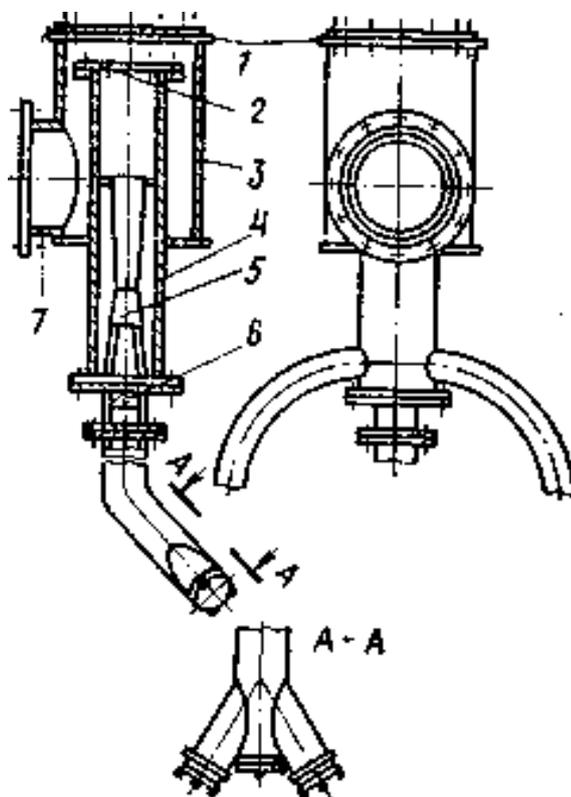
Универсальная пеносливная камера: 1, 2 – крышка; 3 – корпус; 4 – труба; 5 – струйный насадок; 6 – подводящая труба; 7 – патрубок
